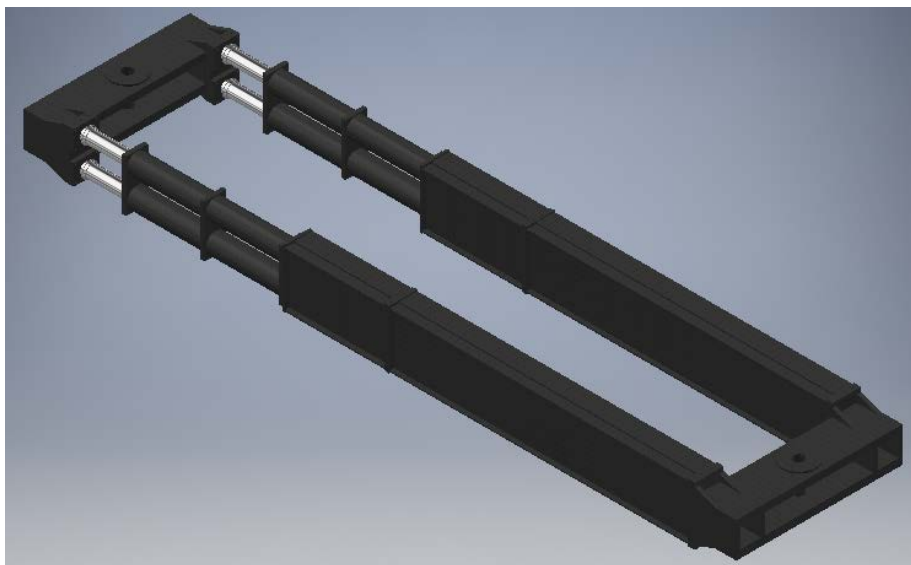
Vista isométrica máquina cabeçotes, pistões e vigas de 3 metros e 9 metros
